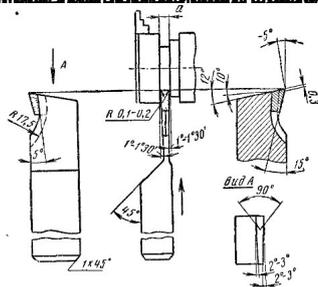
Отрезной твердосплавный резец конструкции В. Солтана
